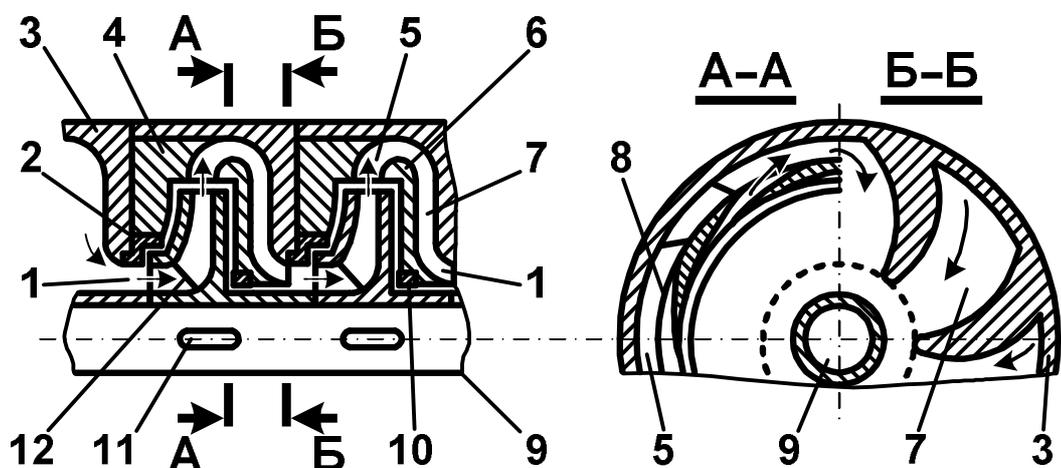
Лопаточный направляющий аппарат: 1 и 7 – подводящие каналы; 2 и 10 – уплотнения; 3 – обойма; 4 и 6 – передняя и задняя перегородки; 5 и 8 – отводящие каналы; 7 – подводящий канал; 9 – вал; 11 – шпонка; 12 – рабочее колесо
